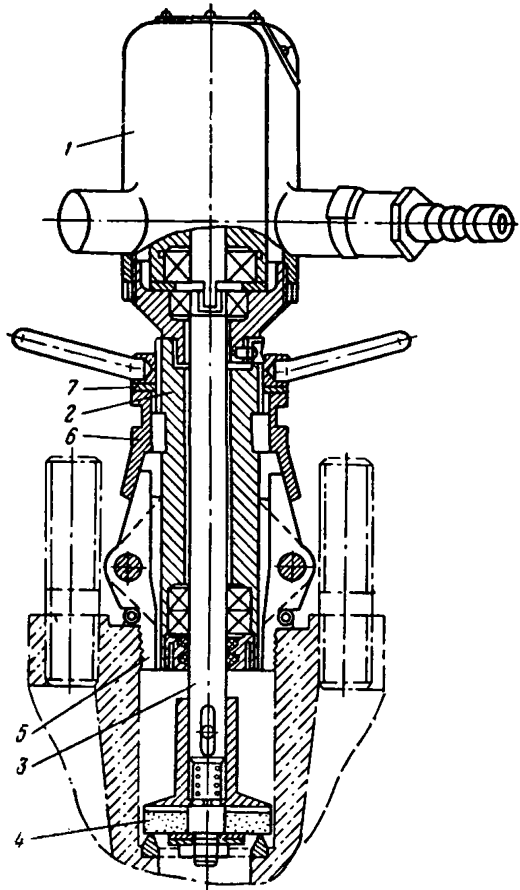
Притирка запорной арматуры с помощью ручного приспособления:
